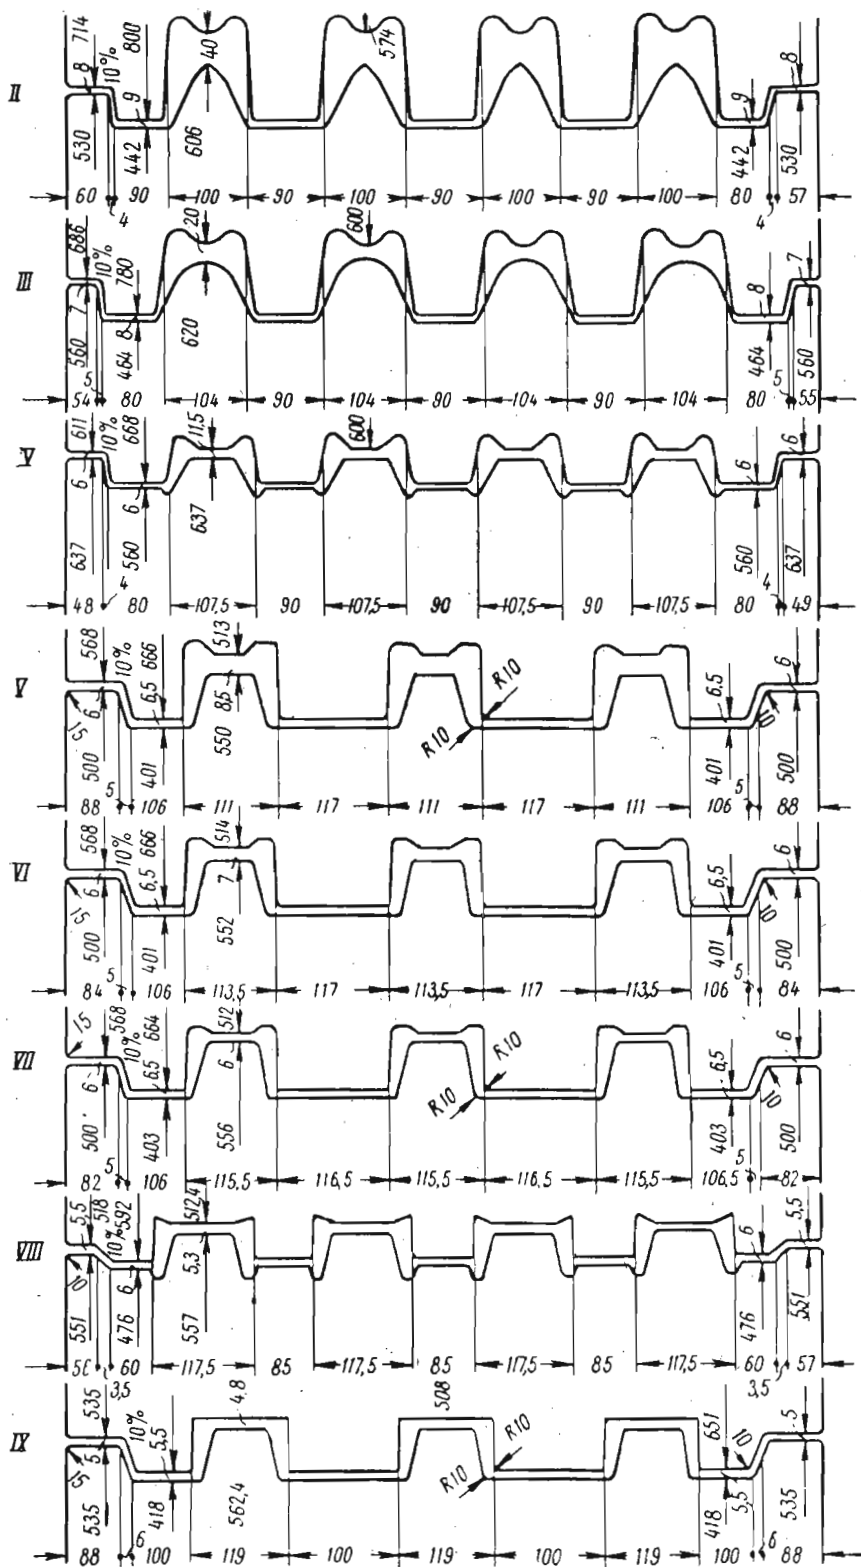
Калибровка валков при прокатке швеллера № 12 на стане 500 (в валки с ящичным калибром клетки I задают разрезную заготовку):
